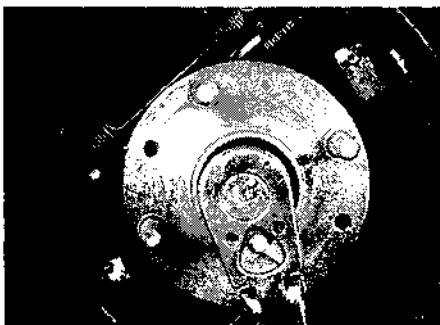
Для снятия ступицы с подшипниками отверните центральную гайку
